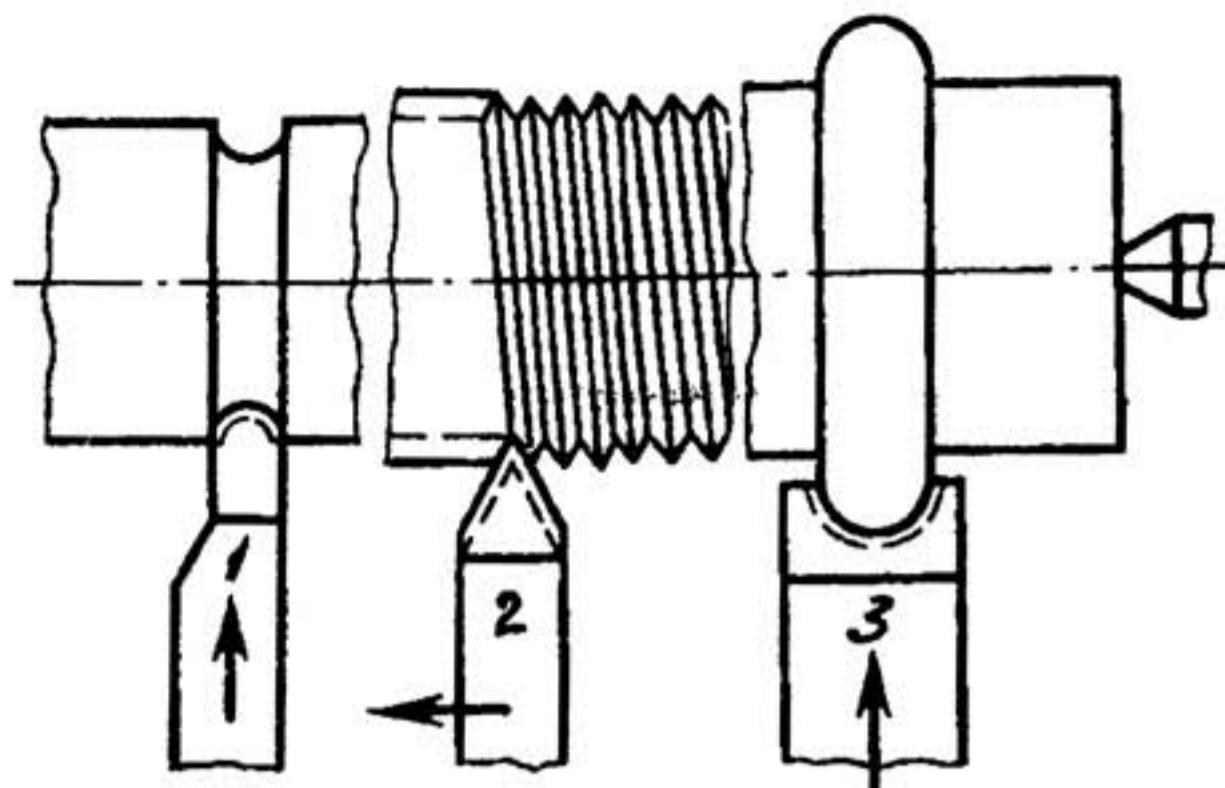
Резцы: галтельный (1), резьбовой (2) и фасонный (3)
